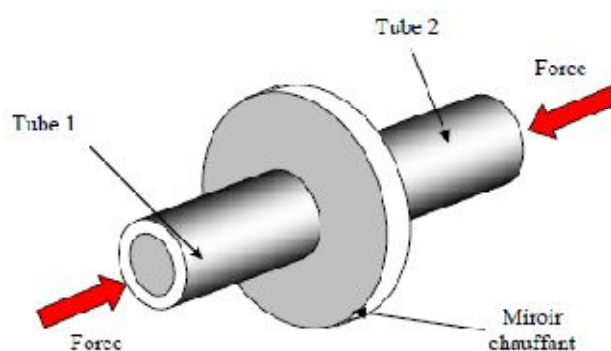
chauffage des tubes lors du soudage bout à bout
